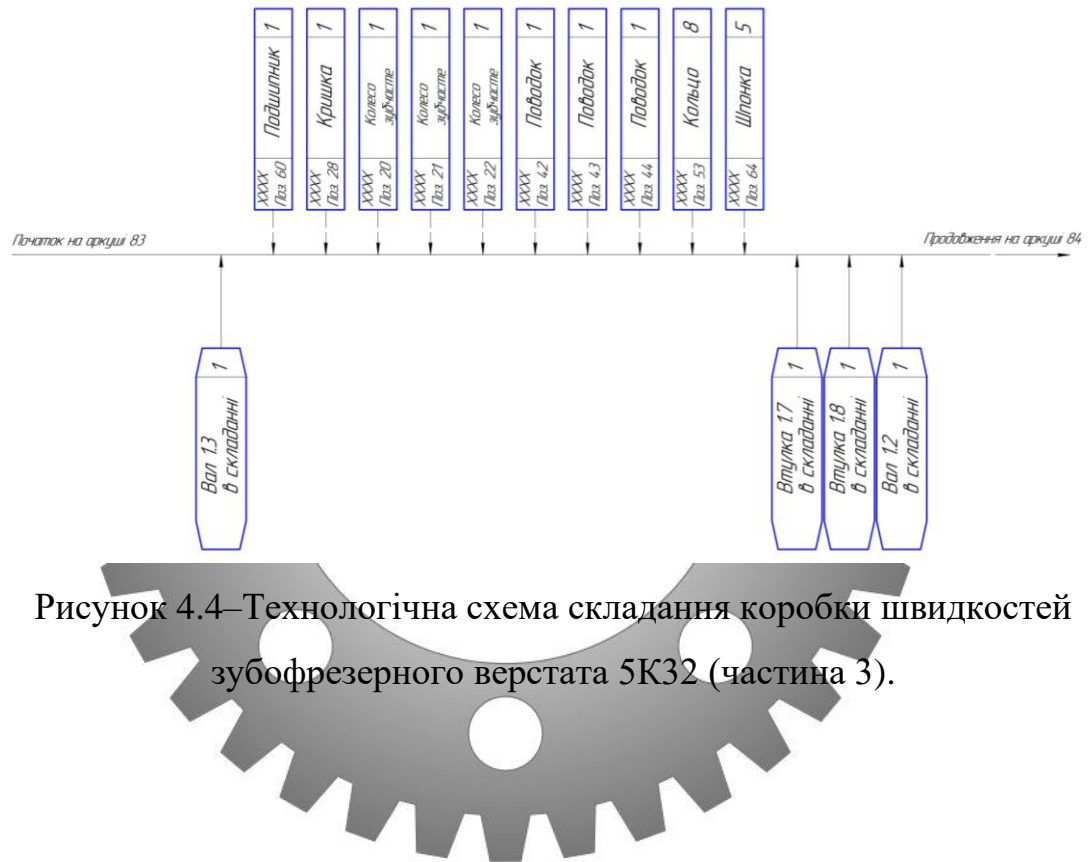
Технологічна схема складання коробки швидкостей зубофрезерного верстата 5К32 (частина 3).
